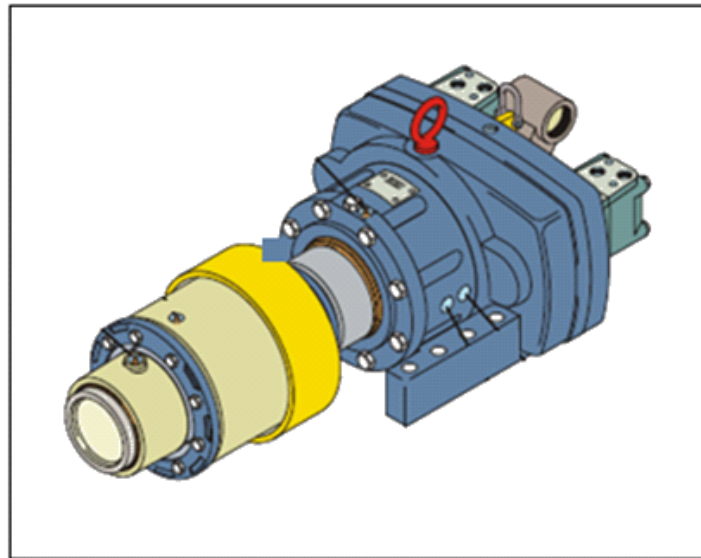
moteur hydraulique de rotation au sommet ROC L 8
